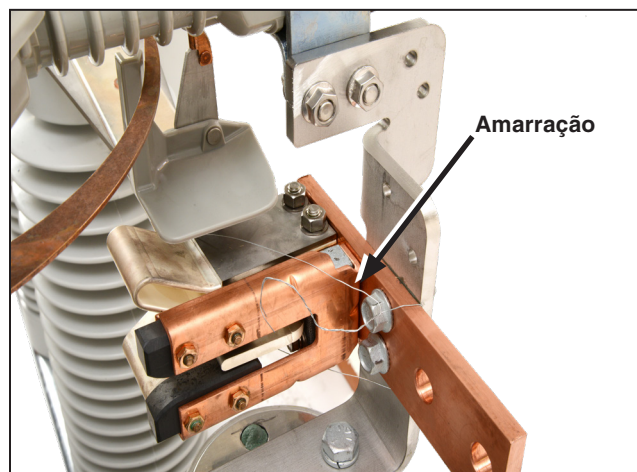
Remova a amarração no conjunto do contato fixo principal.
